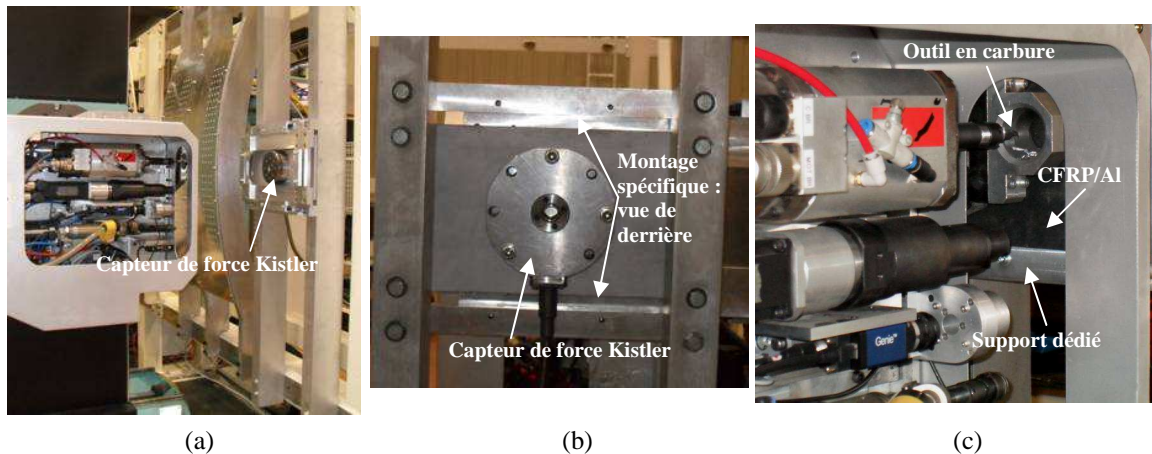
(a) Montage expérimental, (b) fixation du capteur de force sur la colonne de la machine CN, (c) vue de face du montage.
